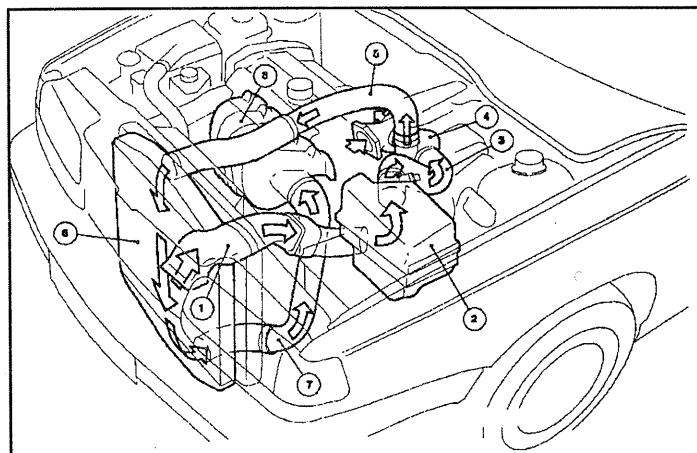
Приток воздуха. Турбодвигатель (1-впускной шланг; 2-корпус воздушного клапана; 3-шланг для свежего воздуха; 4-турбоагрегат; 5-верхняя труба для наддува; 6-радиатор наддувочного воздуха; 7-нижняя труба для наддува; 8-впускной трубопровод).
